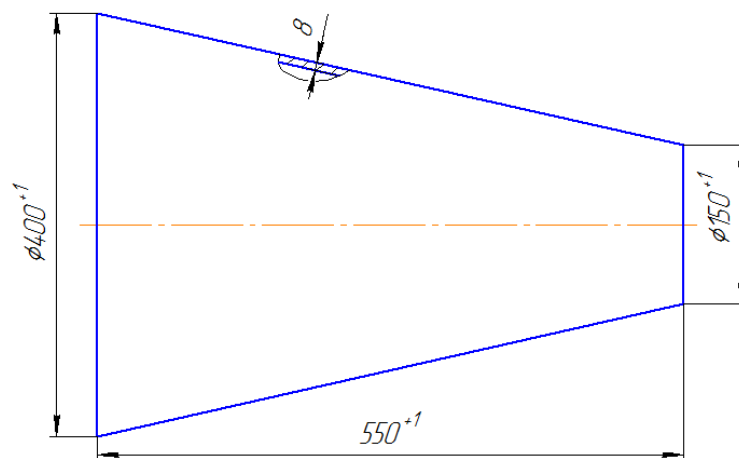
Ескіз корпусу конусної оболонки
